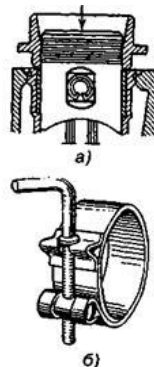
Приспособления для установки поршня с кольцами в цилиндр:
